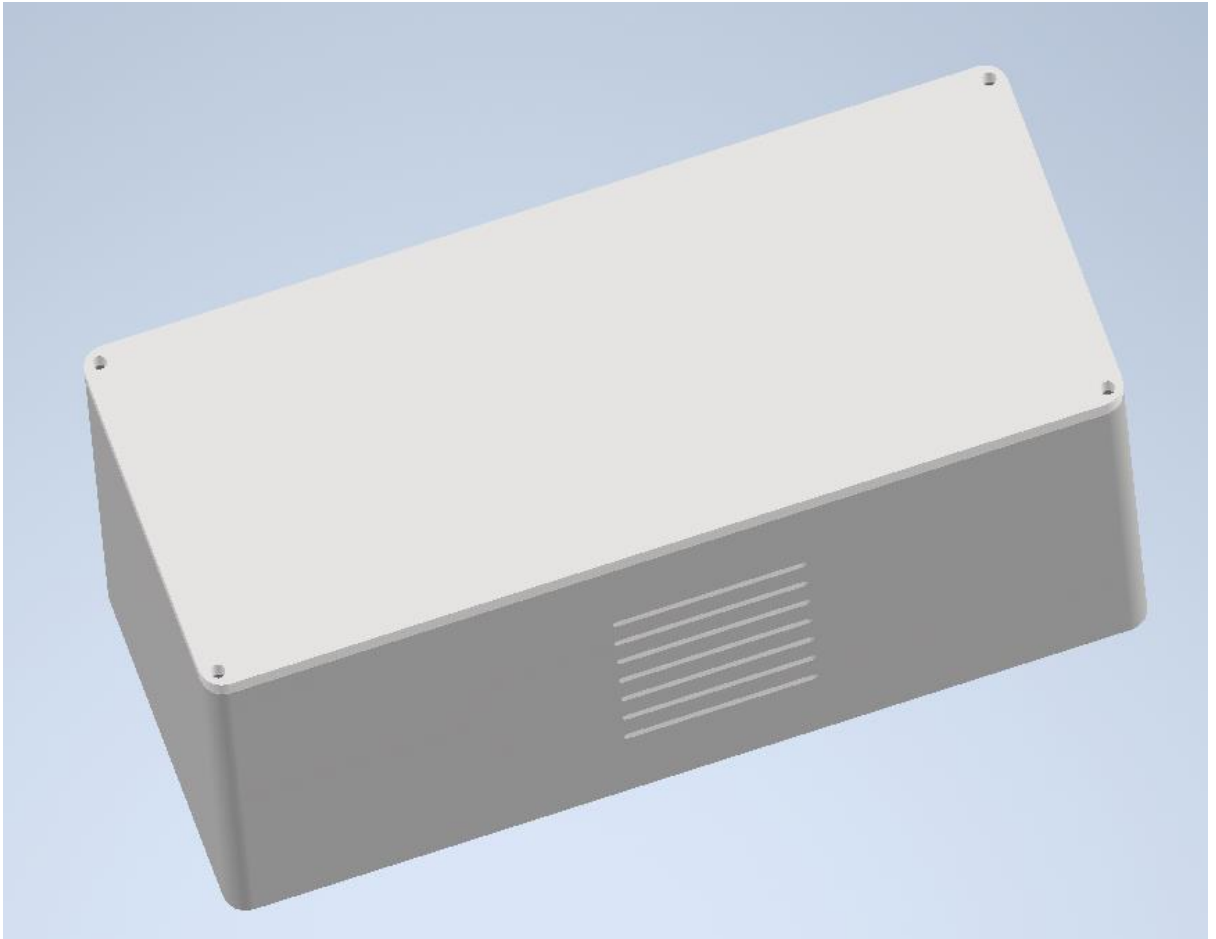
Modelo 3D de la caja que tendrá la PCB y los componentes de control de la PLACA2
